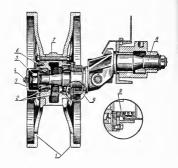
Регулировка подшипников натяжных колес тракторов ЛТ-54. ЛТ-54А и Т-75:
